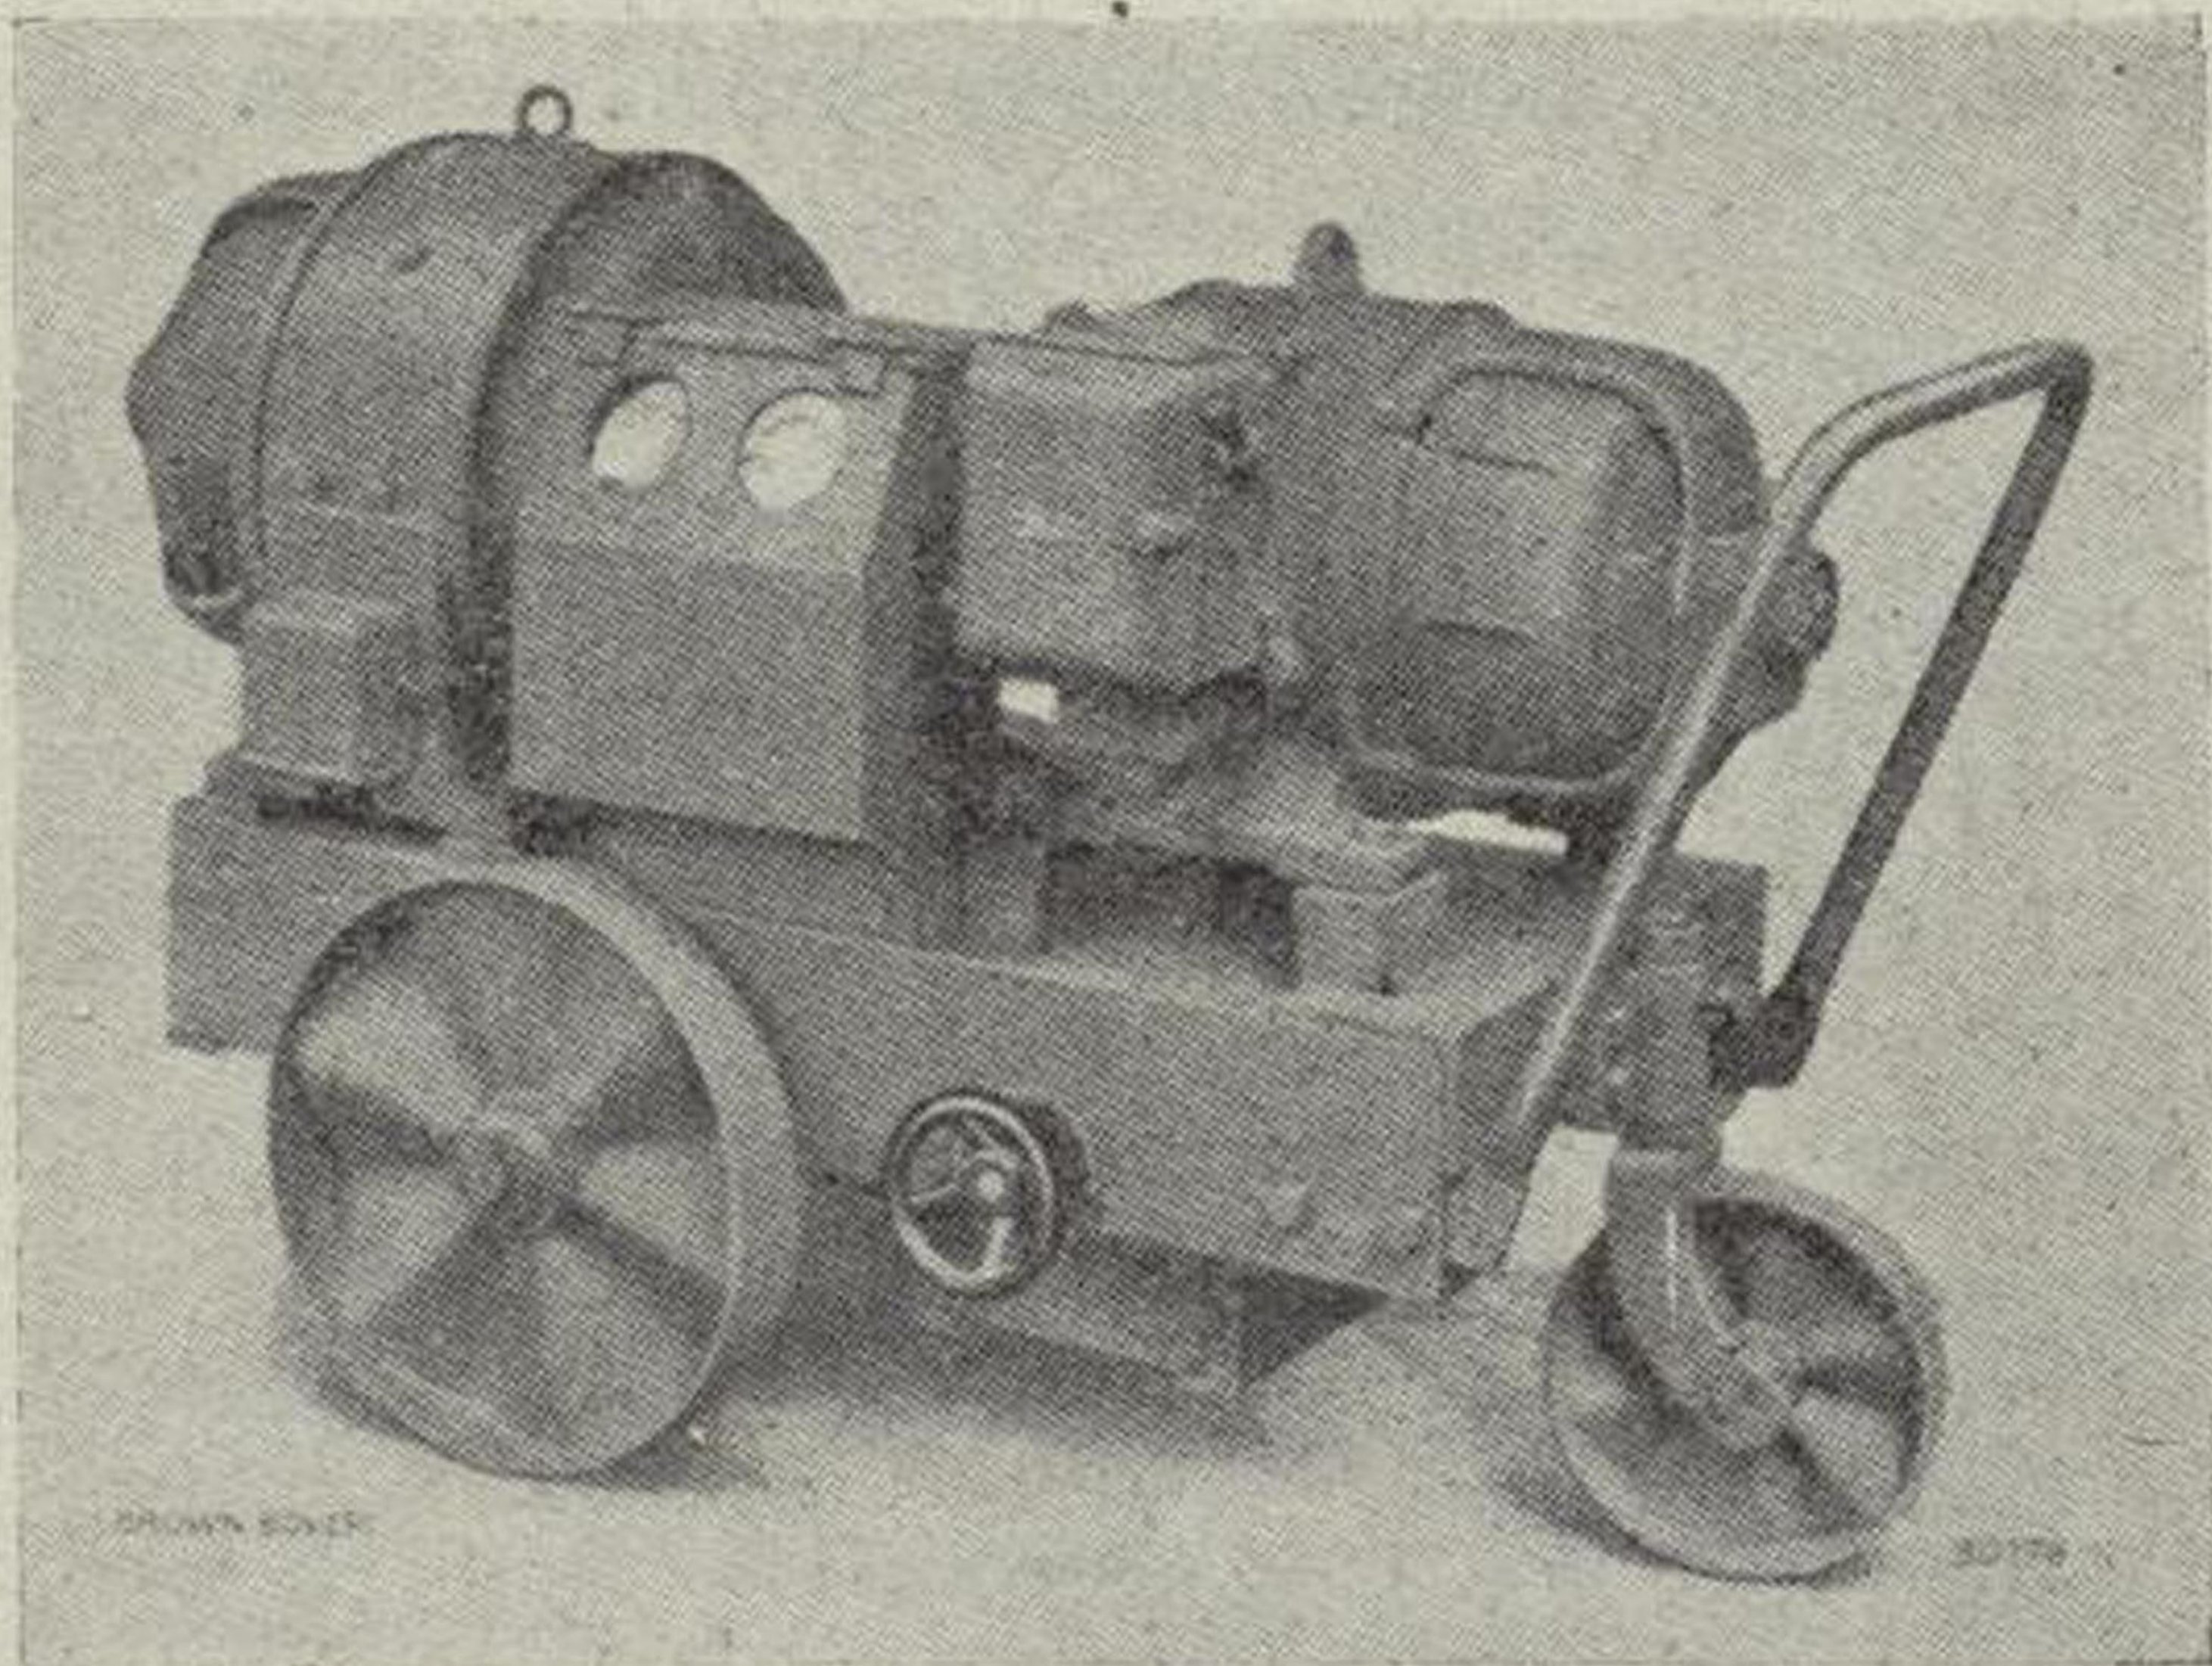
^a—El grupo de soldadura universal Brown Boveri,
